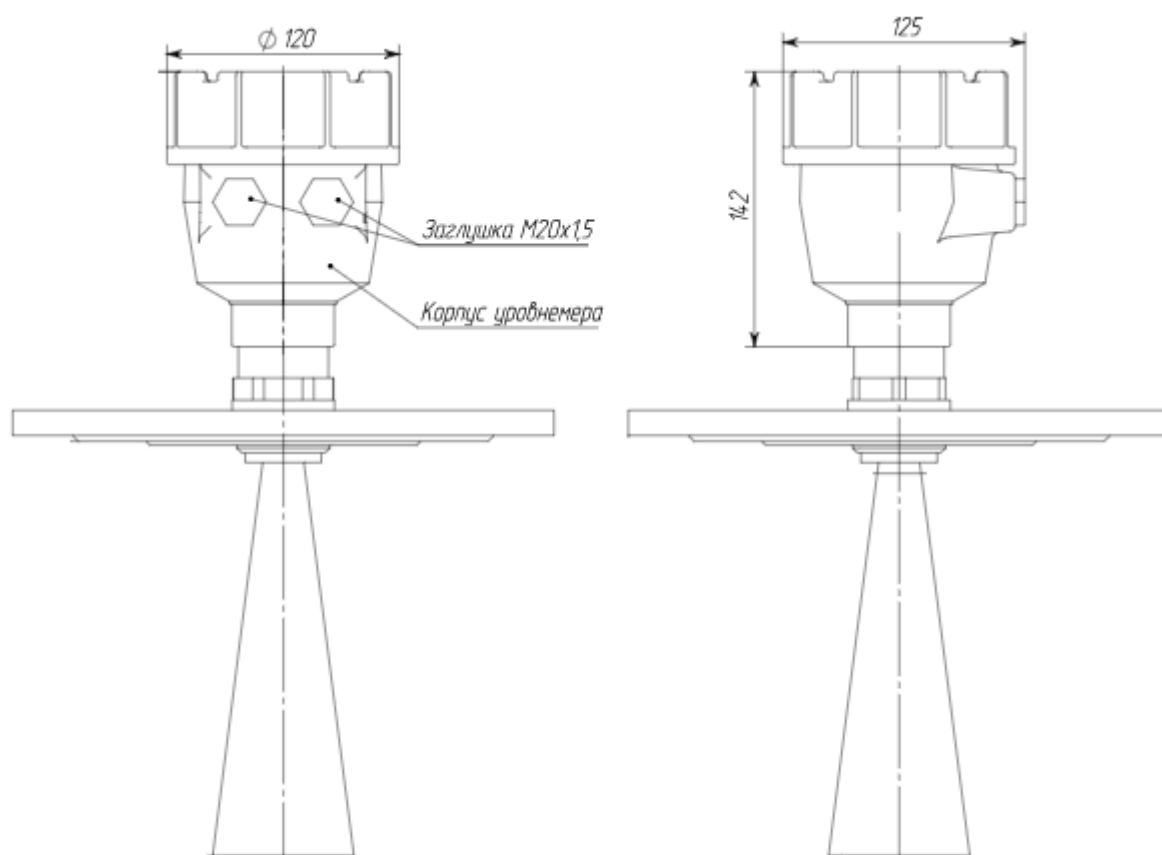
Габаритные размеры корпуса уровнемера
